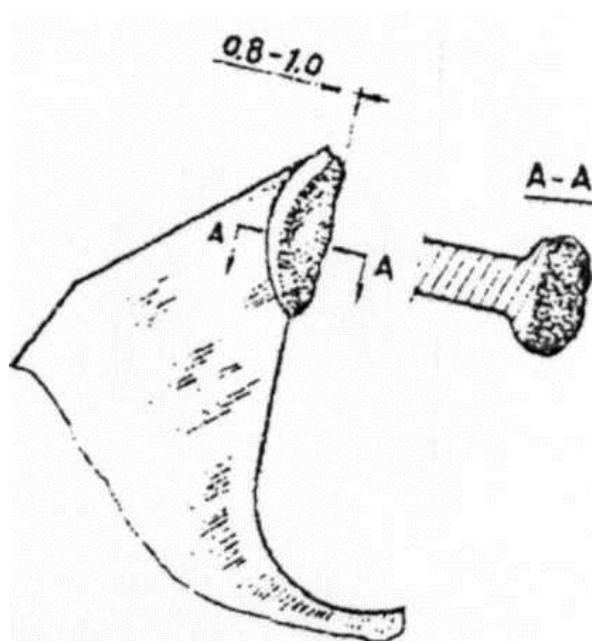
Форма и габариты наплавки стеллита на зуб пилы
